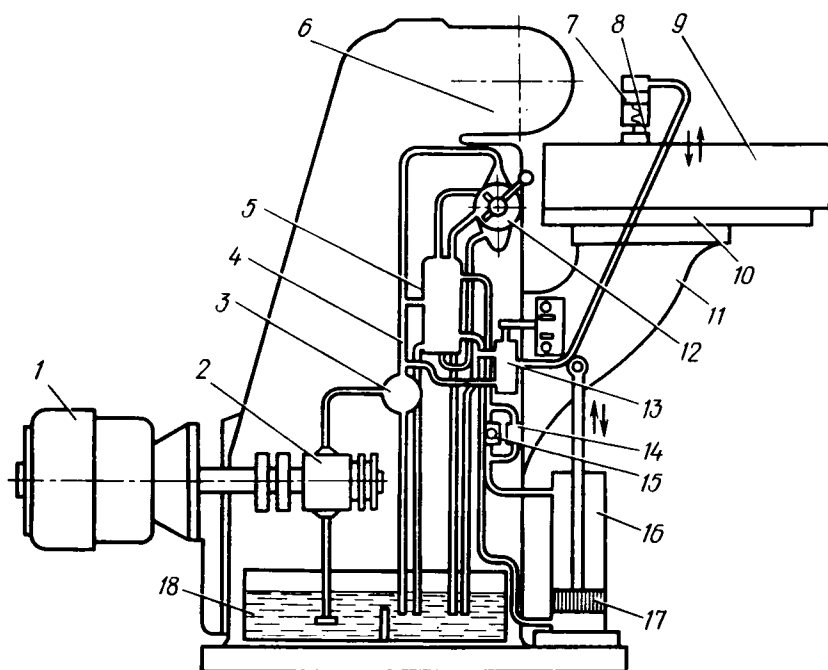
Схема ящичного шипорезного станка ШПК-40:
